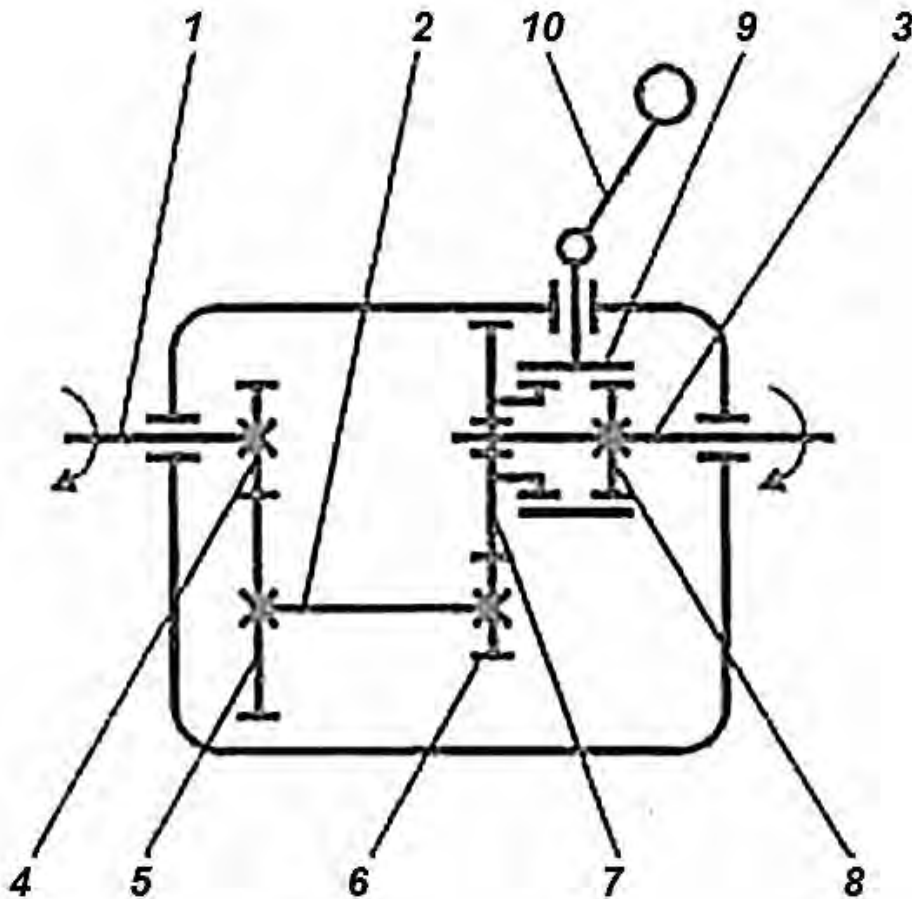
Принципова схема найпростішої коробки передач з шестернями постійного зачеплення:
